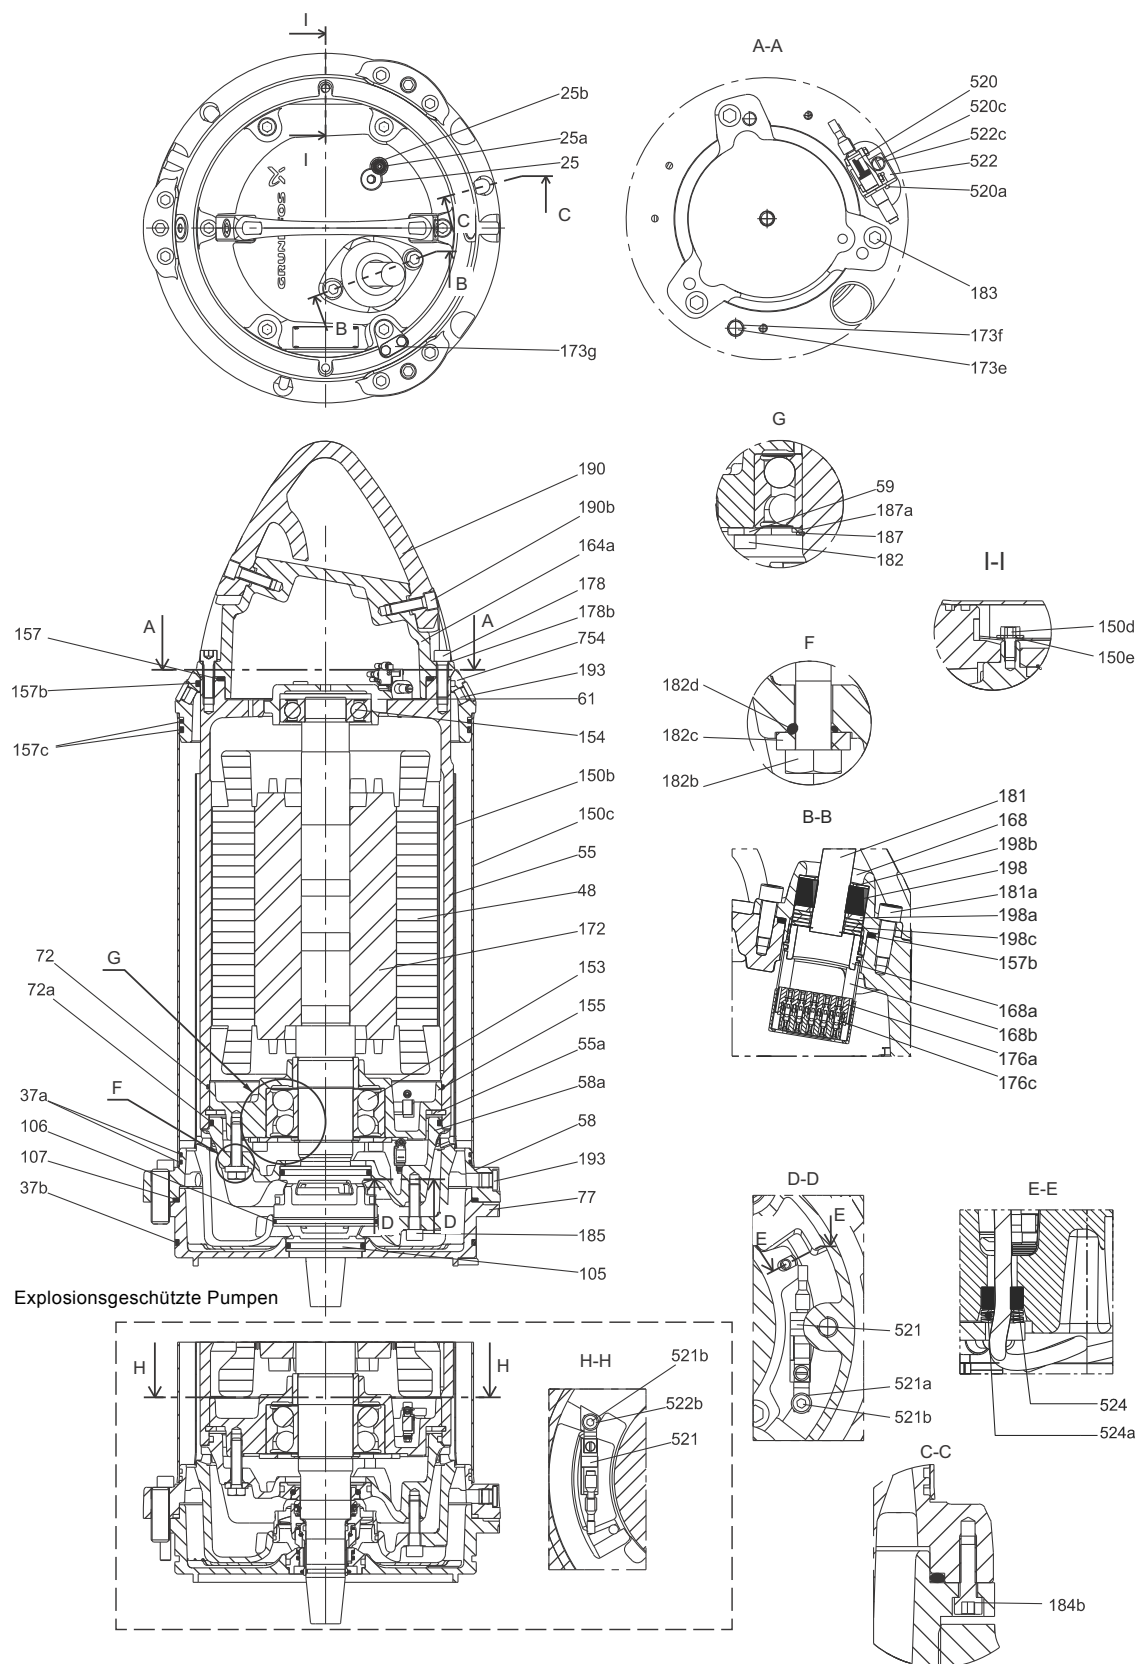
SE-Pumpen mit Kühlmantel mit 2- und 4-poligem Motor
